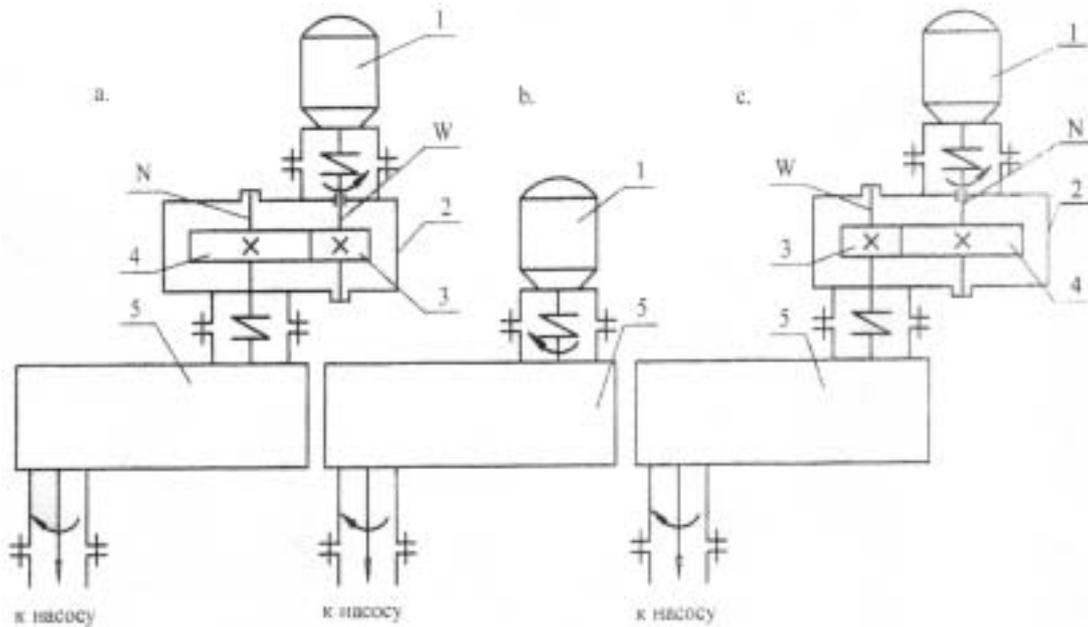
Схемы регулирования частоты вращения колонны штанг с помощью модульной вставки, где: 1 – электродвигатель; 2 – модульная вставка; 3 – зубчатое колесо высокоскоростное; 4 - зубчатое колесо тихоходное; 5 - вращатель (N – тихоходный вал; W – быстроходный вал).
